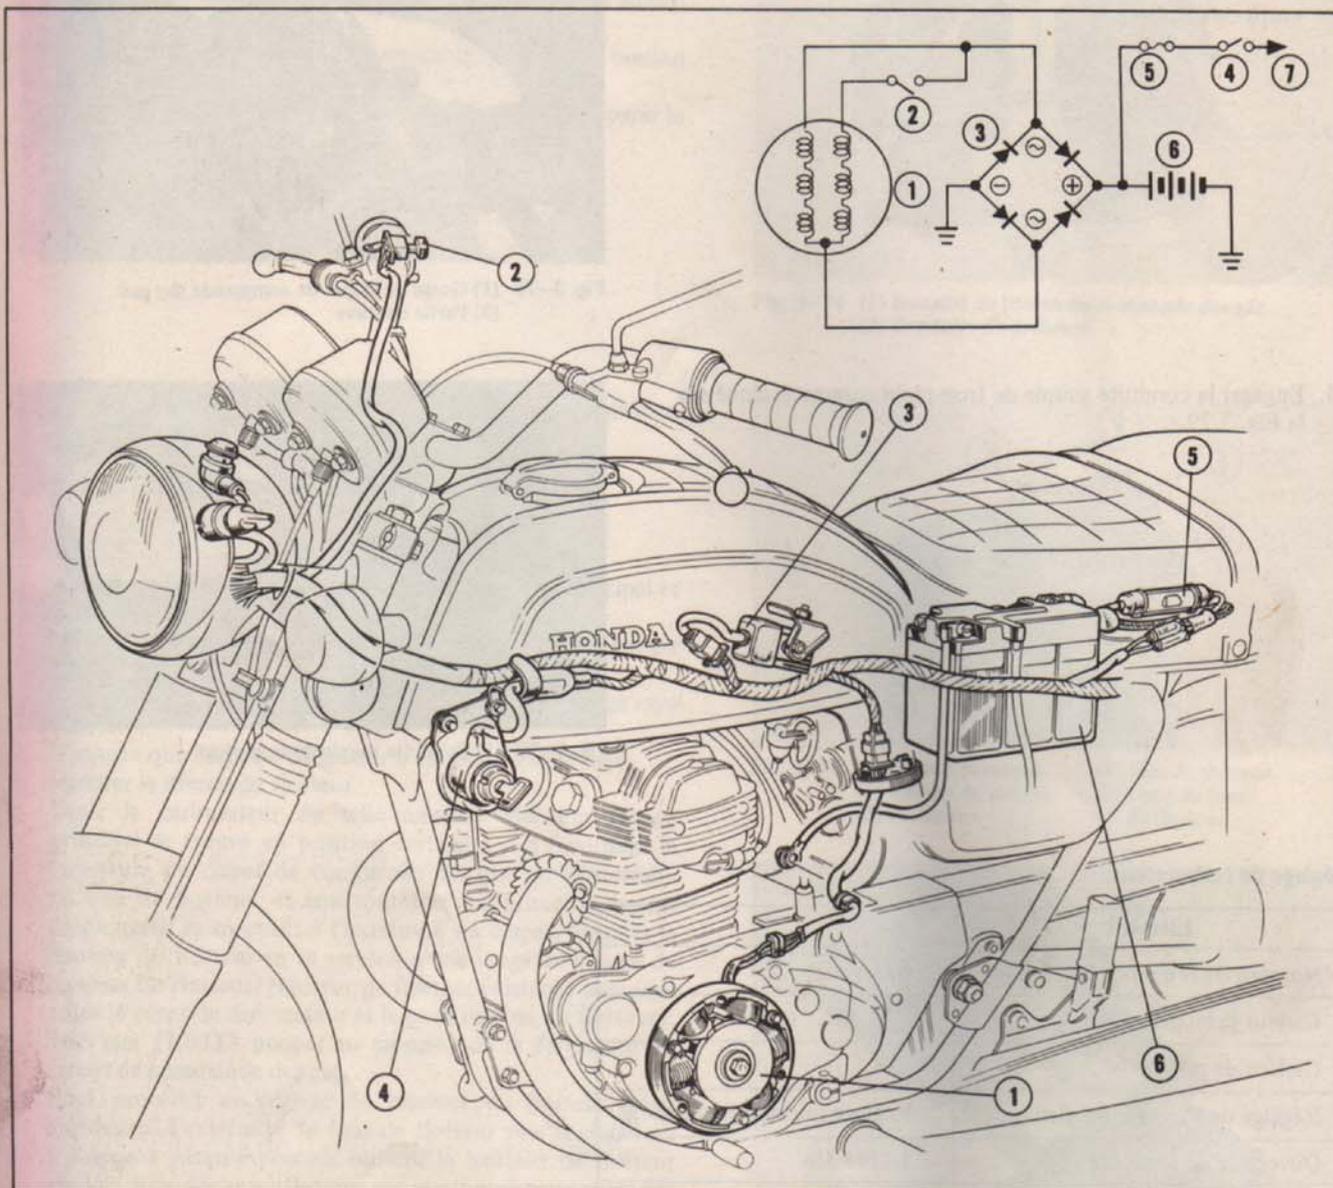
(1) Alternateur (4) Interrupteur général (7) Charge
